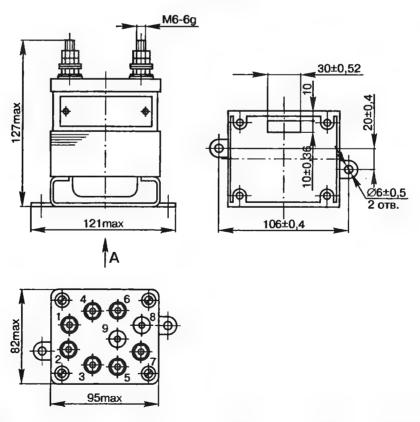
Присоединительные и габаритные размеры трансформаторов CT-5M
